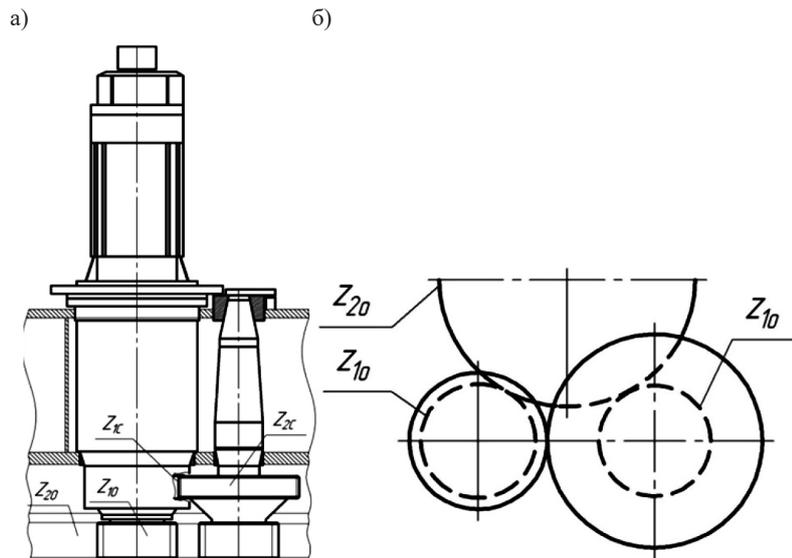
Распределитель механизма поворота перегрузочного крана «Новороссиец»: а — конструкция привода; б — связь обоих приводных валов с колесом ОПУ
